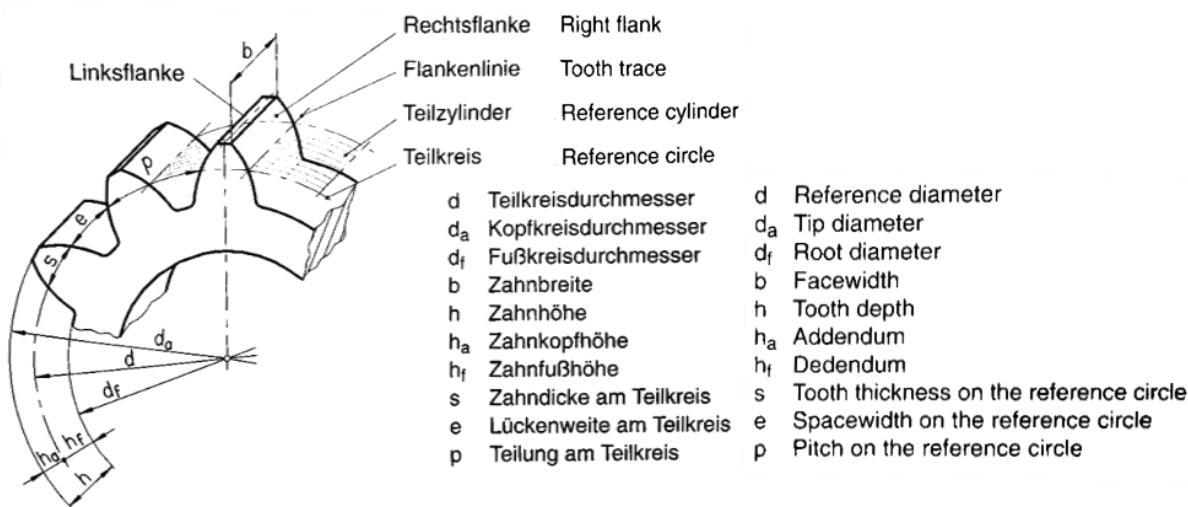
Geometriedaten Geradverzahnung / Geometry of a cylindrical involute gear
